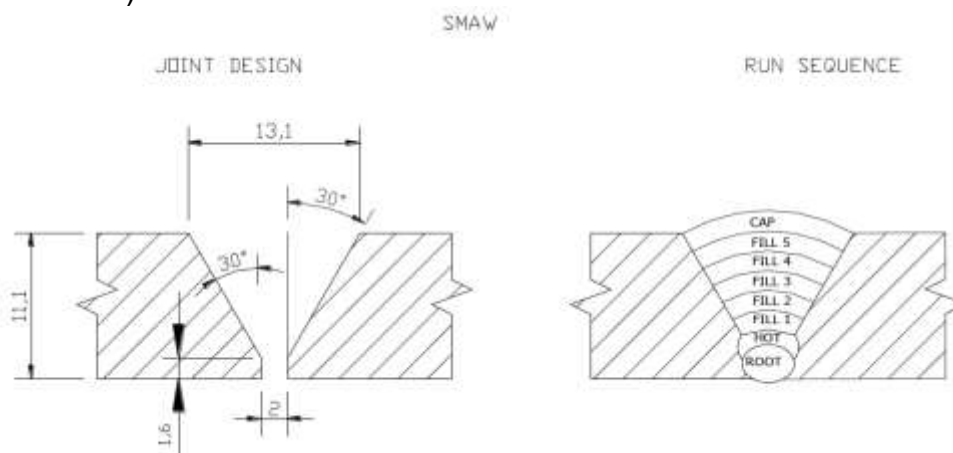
DISEÑO JUNTA Y PASES DE SOLDADURA TECNOLOGÍA SMAW
